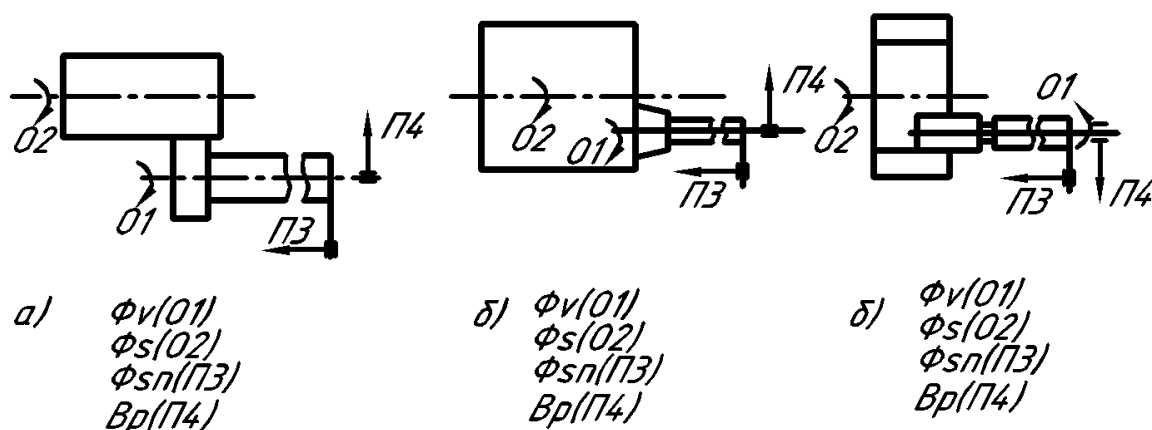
Класичні схеми формоутворення зовнішніх та внутрішніх циліндричних поверхонь фінішною обробкою.
